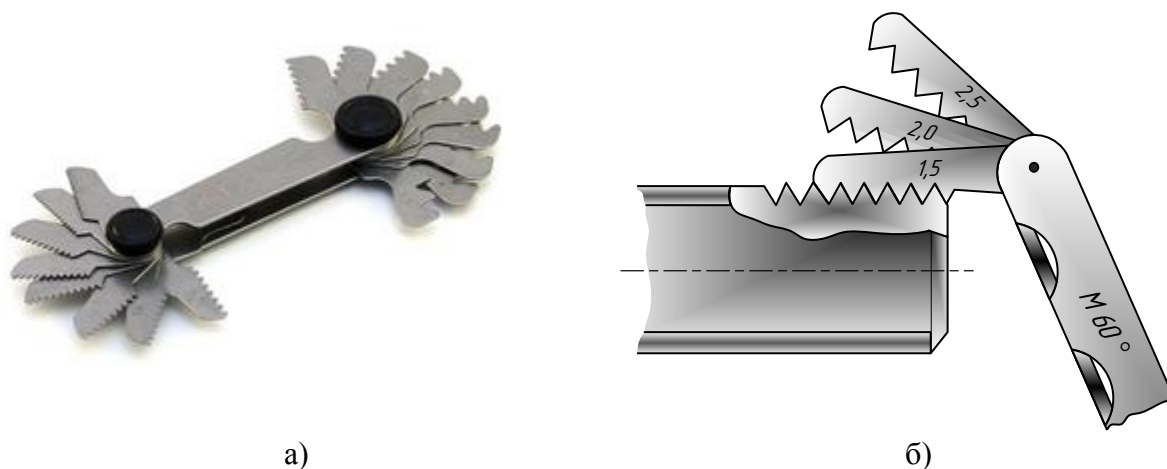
Резьбовой шаблон и схема определения номинального шага резьбы с помощью резьбового шаблона
